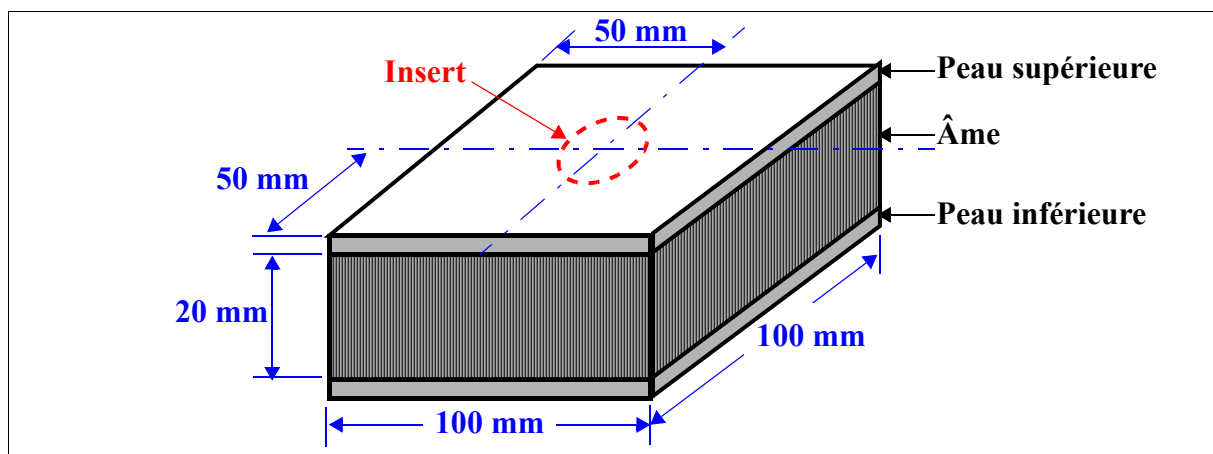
Géométrie et dimensions de l'éprouvette.
